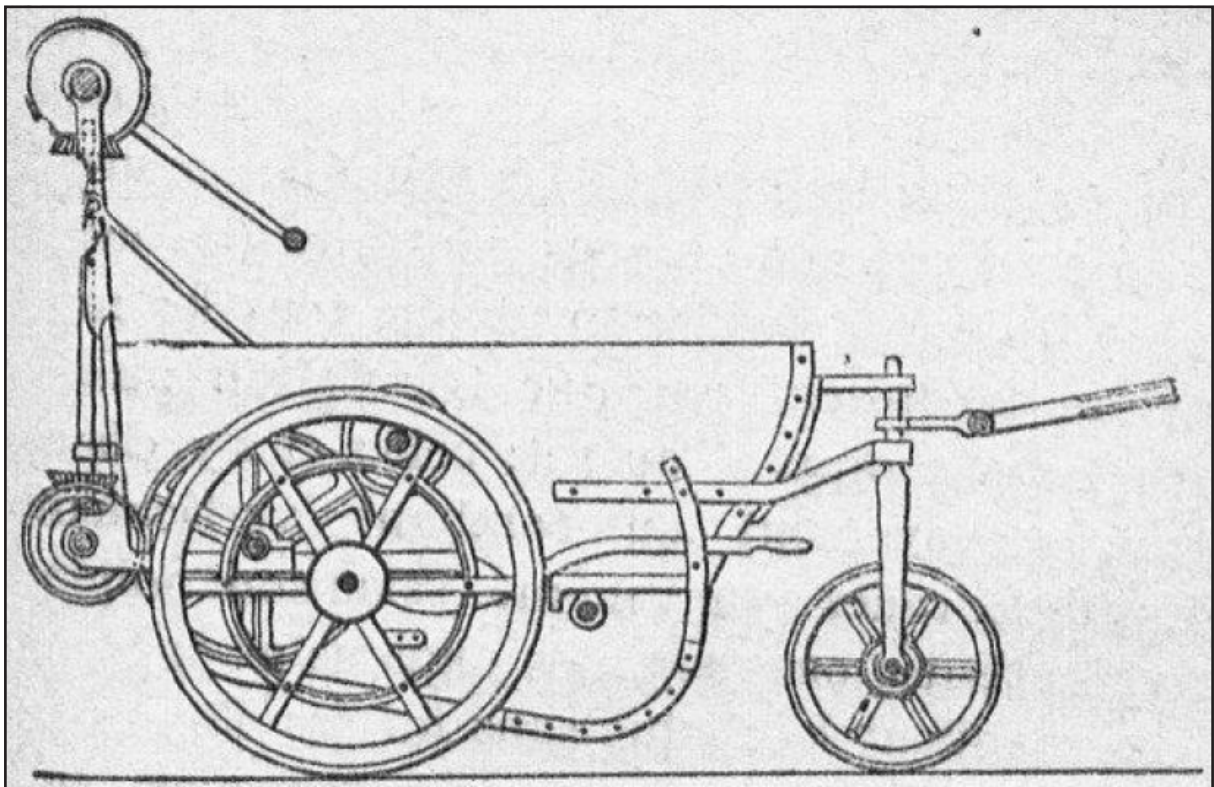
Dessin d'une mouleuse mécanique (source : Guieu P., 1918)
